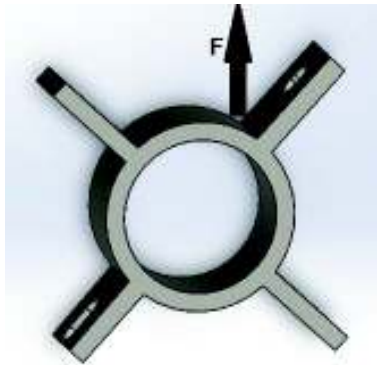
Fuerza que actúa sobre el elemento soldado.
